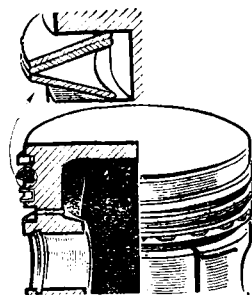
Размещение поршневых колец в канавках поршня двигателя легкового автомобиля
